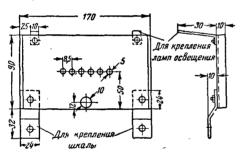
Устройство шасси и расположение деталей приемника РЛ-3.
